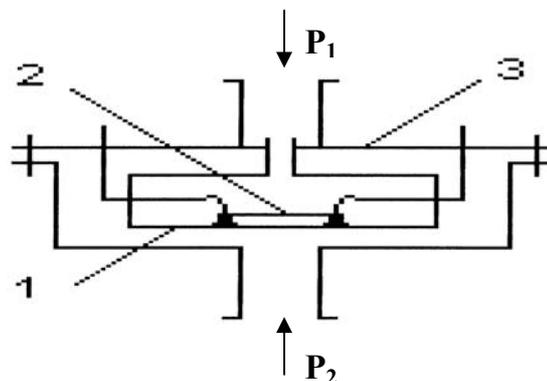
Схема конструкции датчика давления: 1-мембранно-преобразующий узел; 2-резонатор; 3- корпус с патрубками
